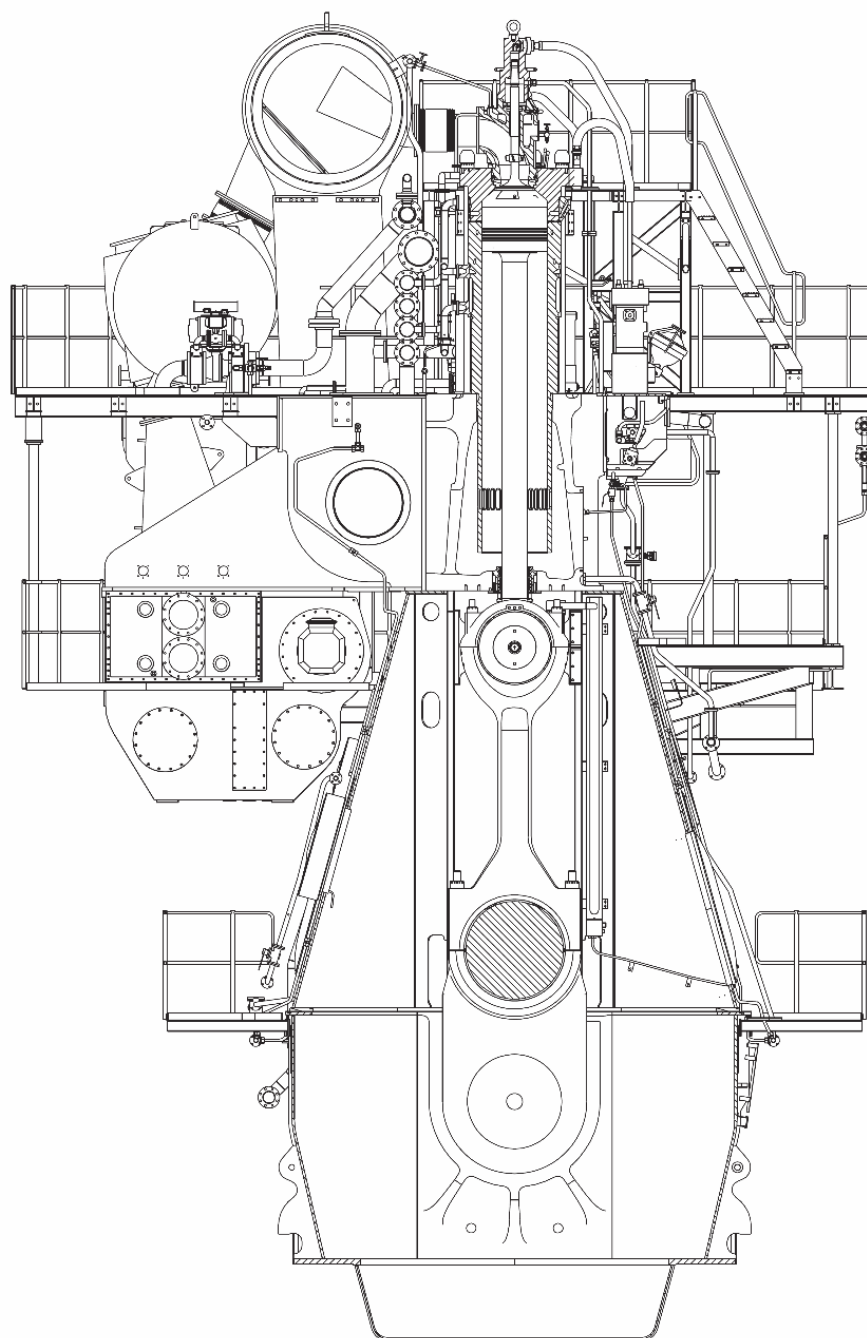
Поперечний розріз головного суднового двигуна 6G60ME-C9
